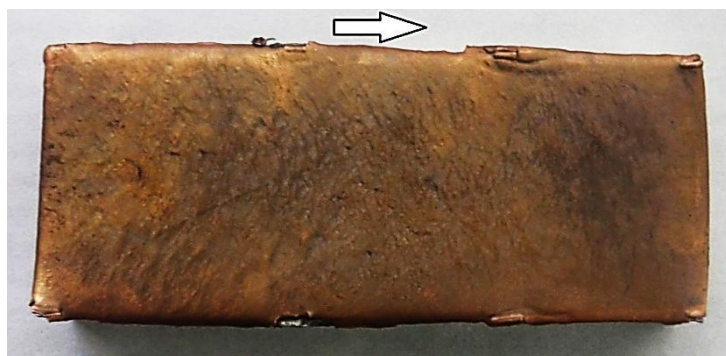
Nova soldadura SE1_25/15.
